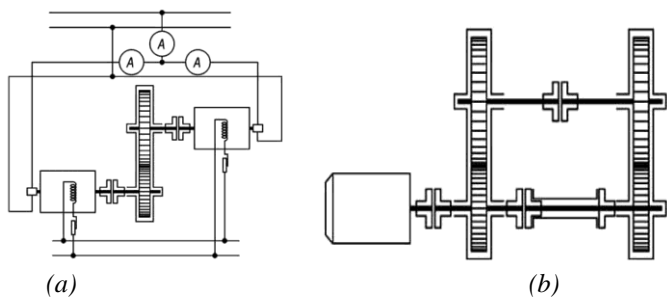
Máquina para el ensayo de engranajes con lazo de potencia cerrado, a) Eléctrico, b) Mecánico [14].
